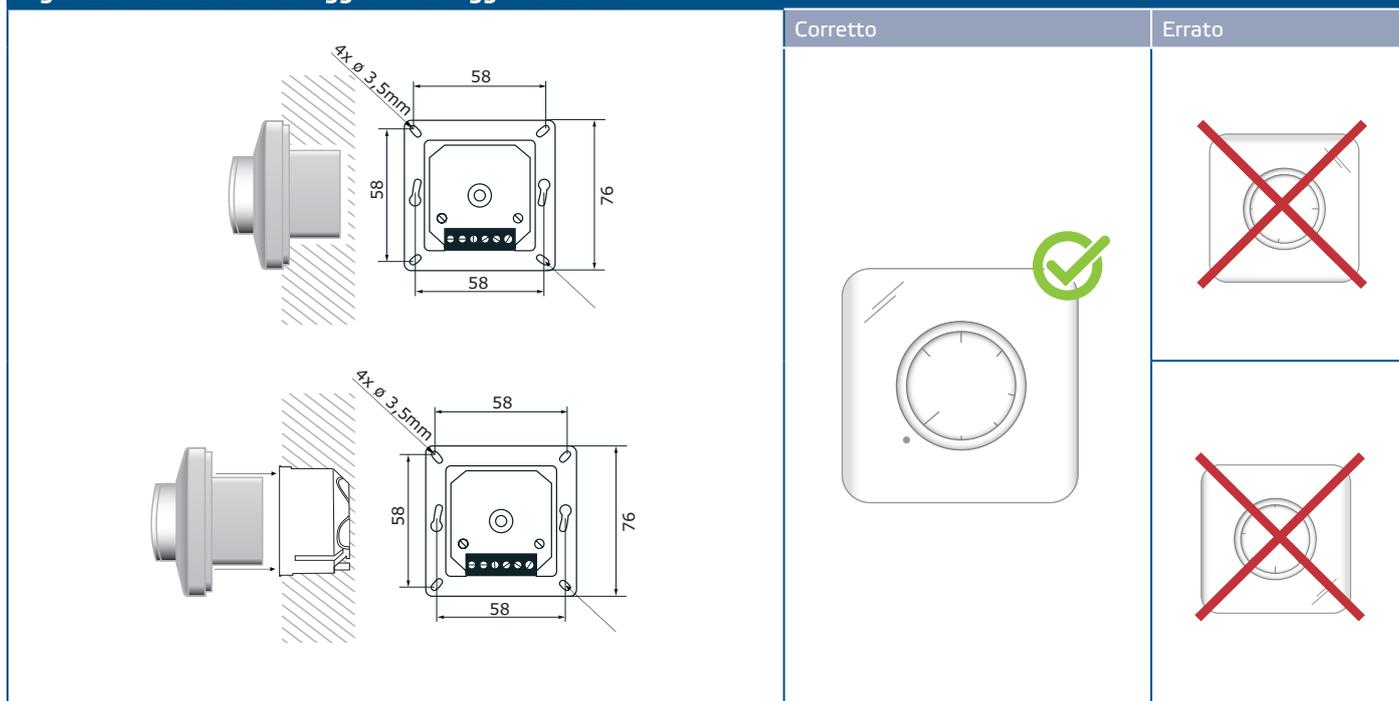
Dimensioni di montaggio - montaggio ad incasso
